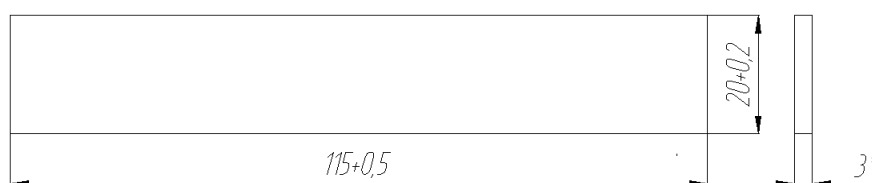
Образец для испытаний на сжатие, ГОСТ 4651 [3]
